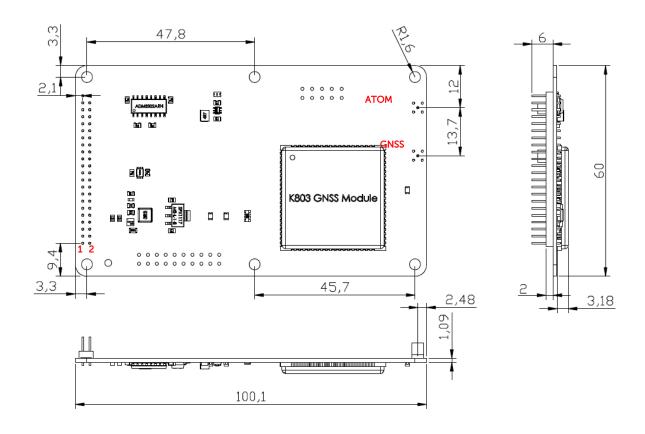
Размеры ГНСС-приемников 4GNSS типоразмера S60100 NP1/NP2/NP3/NP3I
